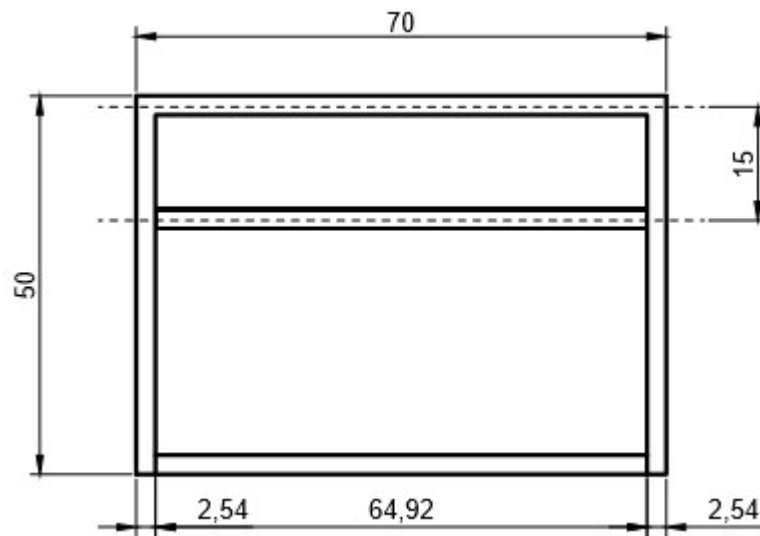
Vista izquierda de estructura con recubierto de hoja de lata
